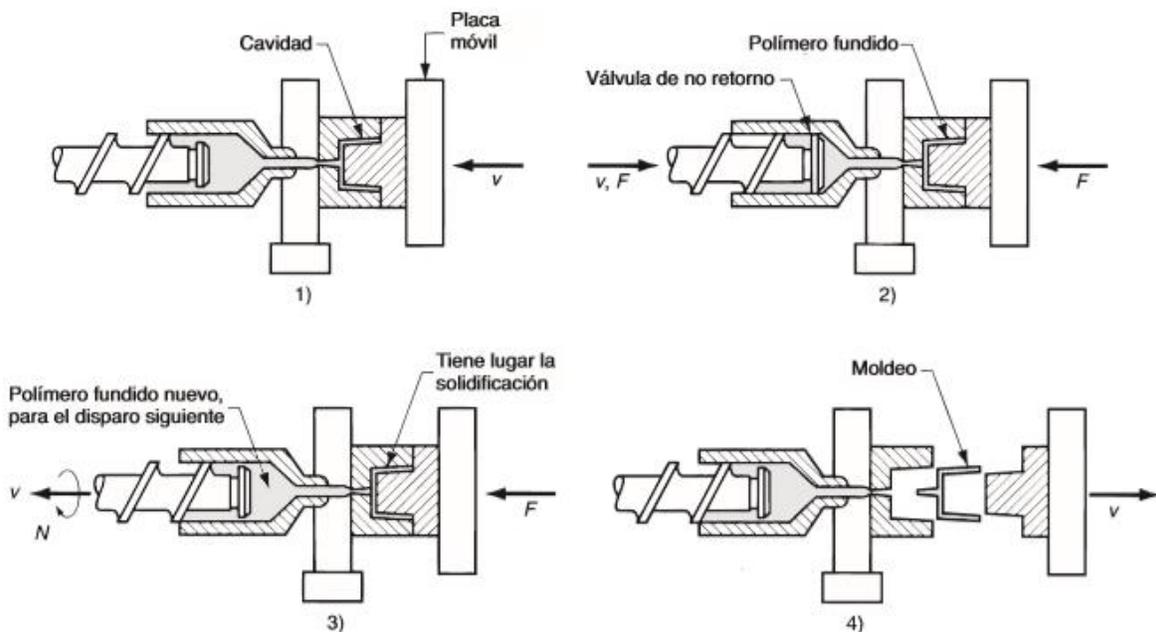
Ciclo común de moldeo: 1) molde cerrado, 2) se inyecta fluido a la cavidad, 3) se retrae el tornillo y 4) se abre el molde, y la pieza se expulsa.
